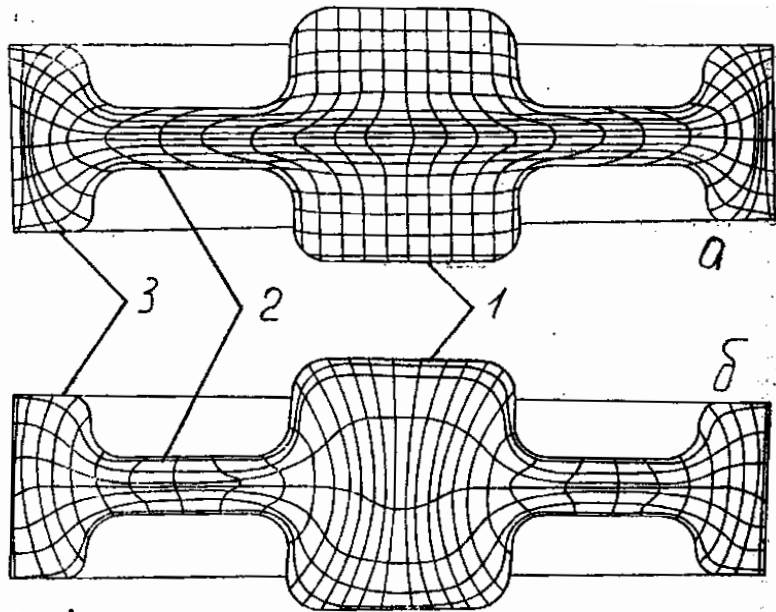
Характер течії металу при штампуванні із заготовки деталей типу шестерні з H_0/D_0 : а - 2,0...2,5; б - <1; 1 - маточина; 2 - диск; 3 - обід
